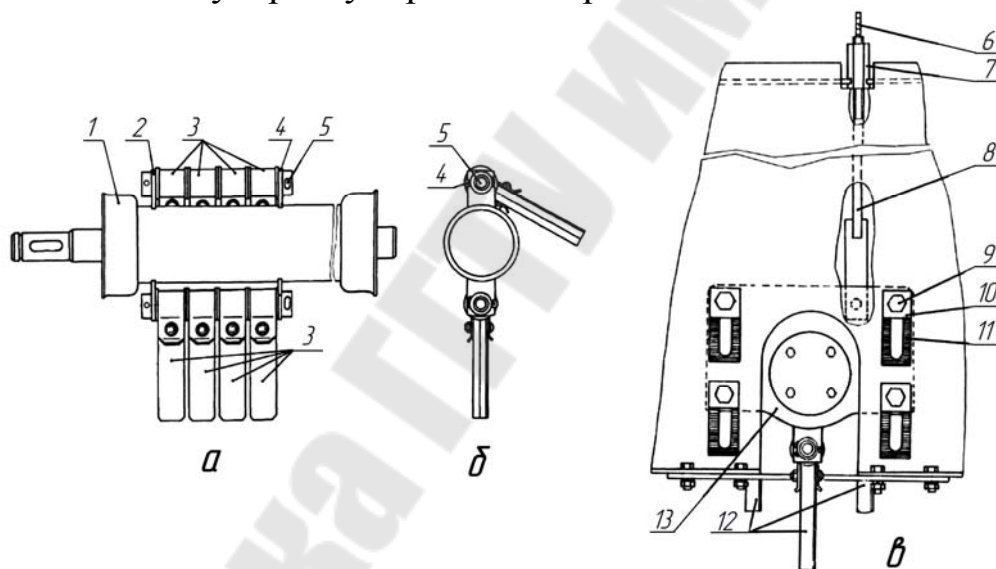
Очиститель головок корней: а – очиститель (вид сбоку); б – механизм регулировки очищающего вала по высоте (вид сзади); 1 – вал; 2, 5 – опоры; 3, 12 – очистители; 4 – шплинт; 6 – линейка; 7 – винт регулировочный; 8 – тяга; 9 – болт; 10 – шайба рифленая; 11 – щека; 13 – корпус подшипника
